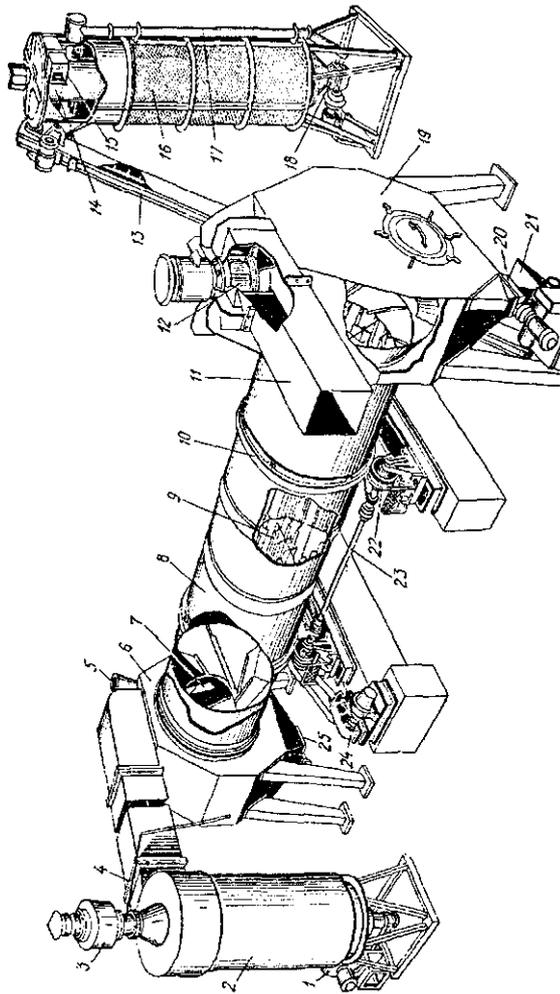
Загальний вид зерносушарки СЗСБ-8:
